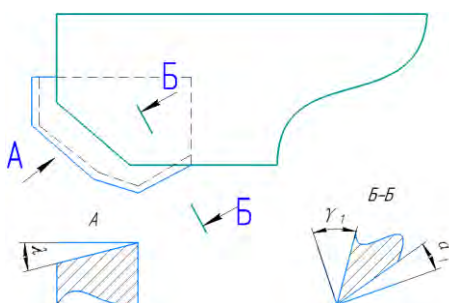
Вспомогательный задний угол α_1 и положительный угол наклона главной режущей кромки λ фрезы [2]
